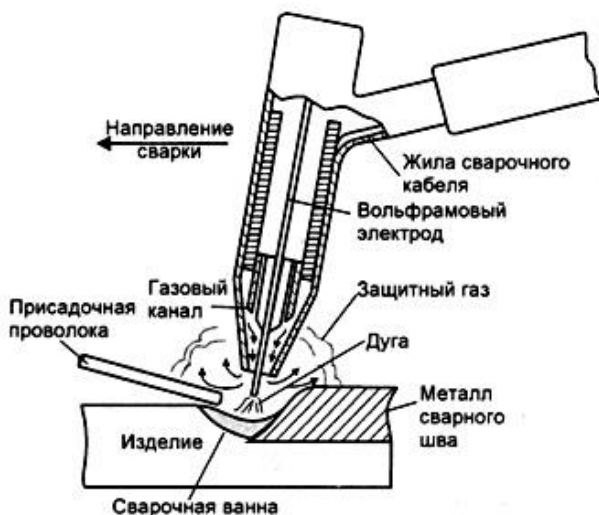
Схема сварки вольфрамовым электродом в среде защитного газа
